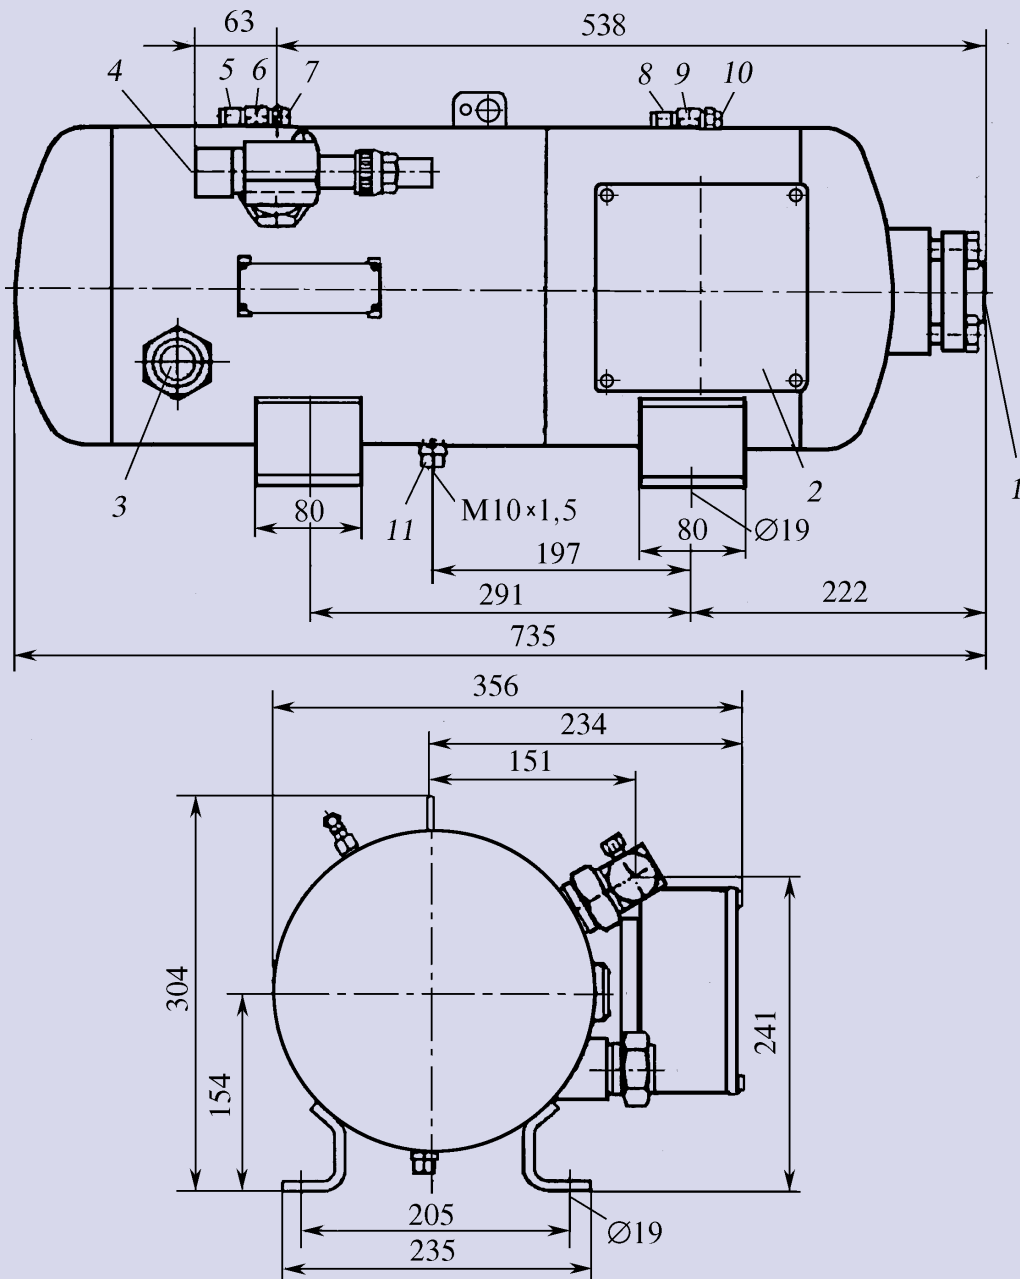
Герметичный винтовой холодильный компрессор VSK 3161-15Y:
